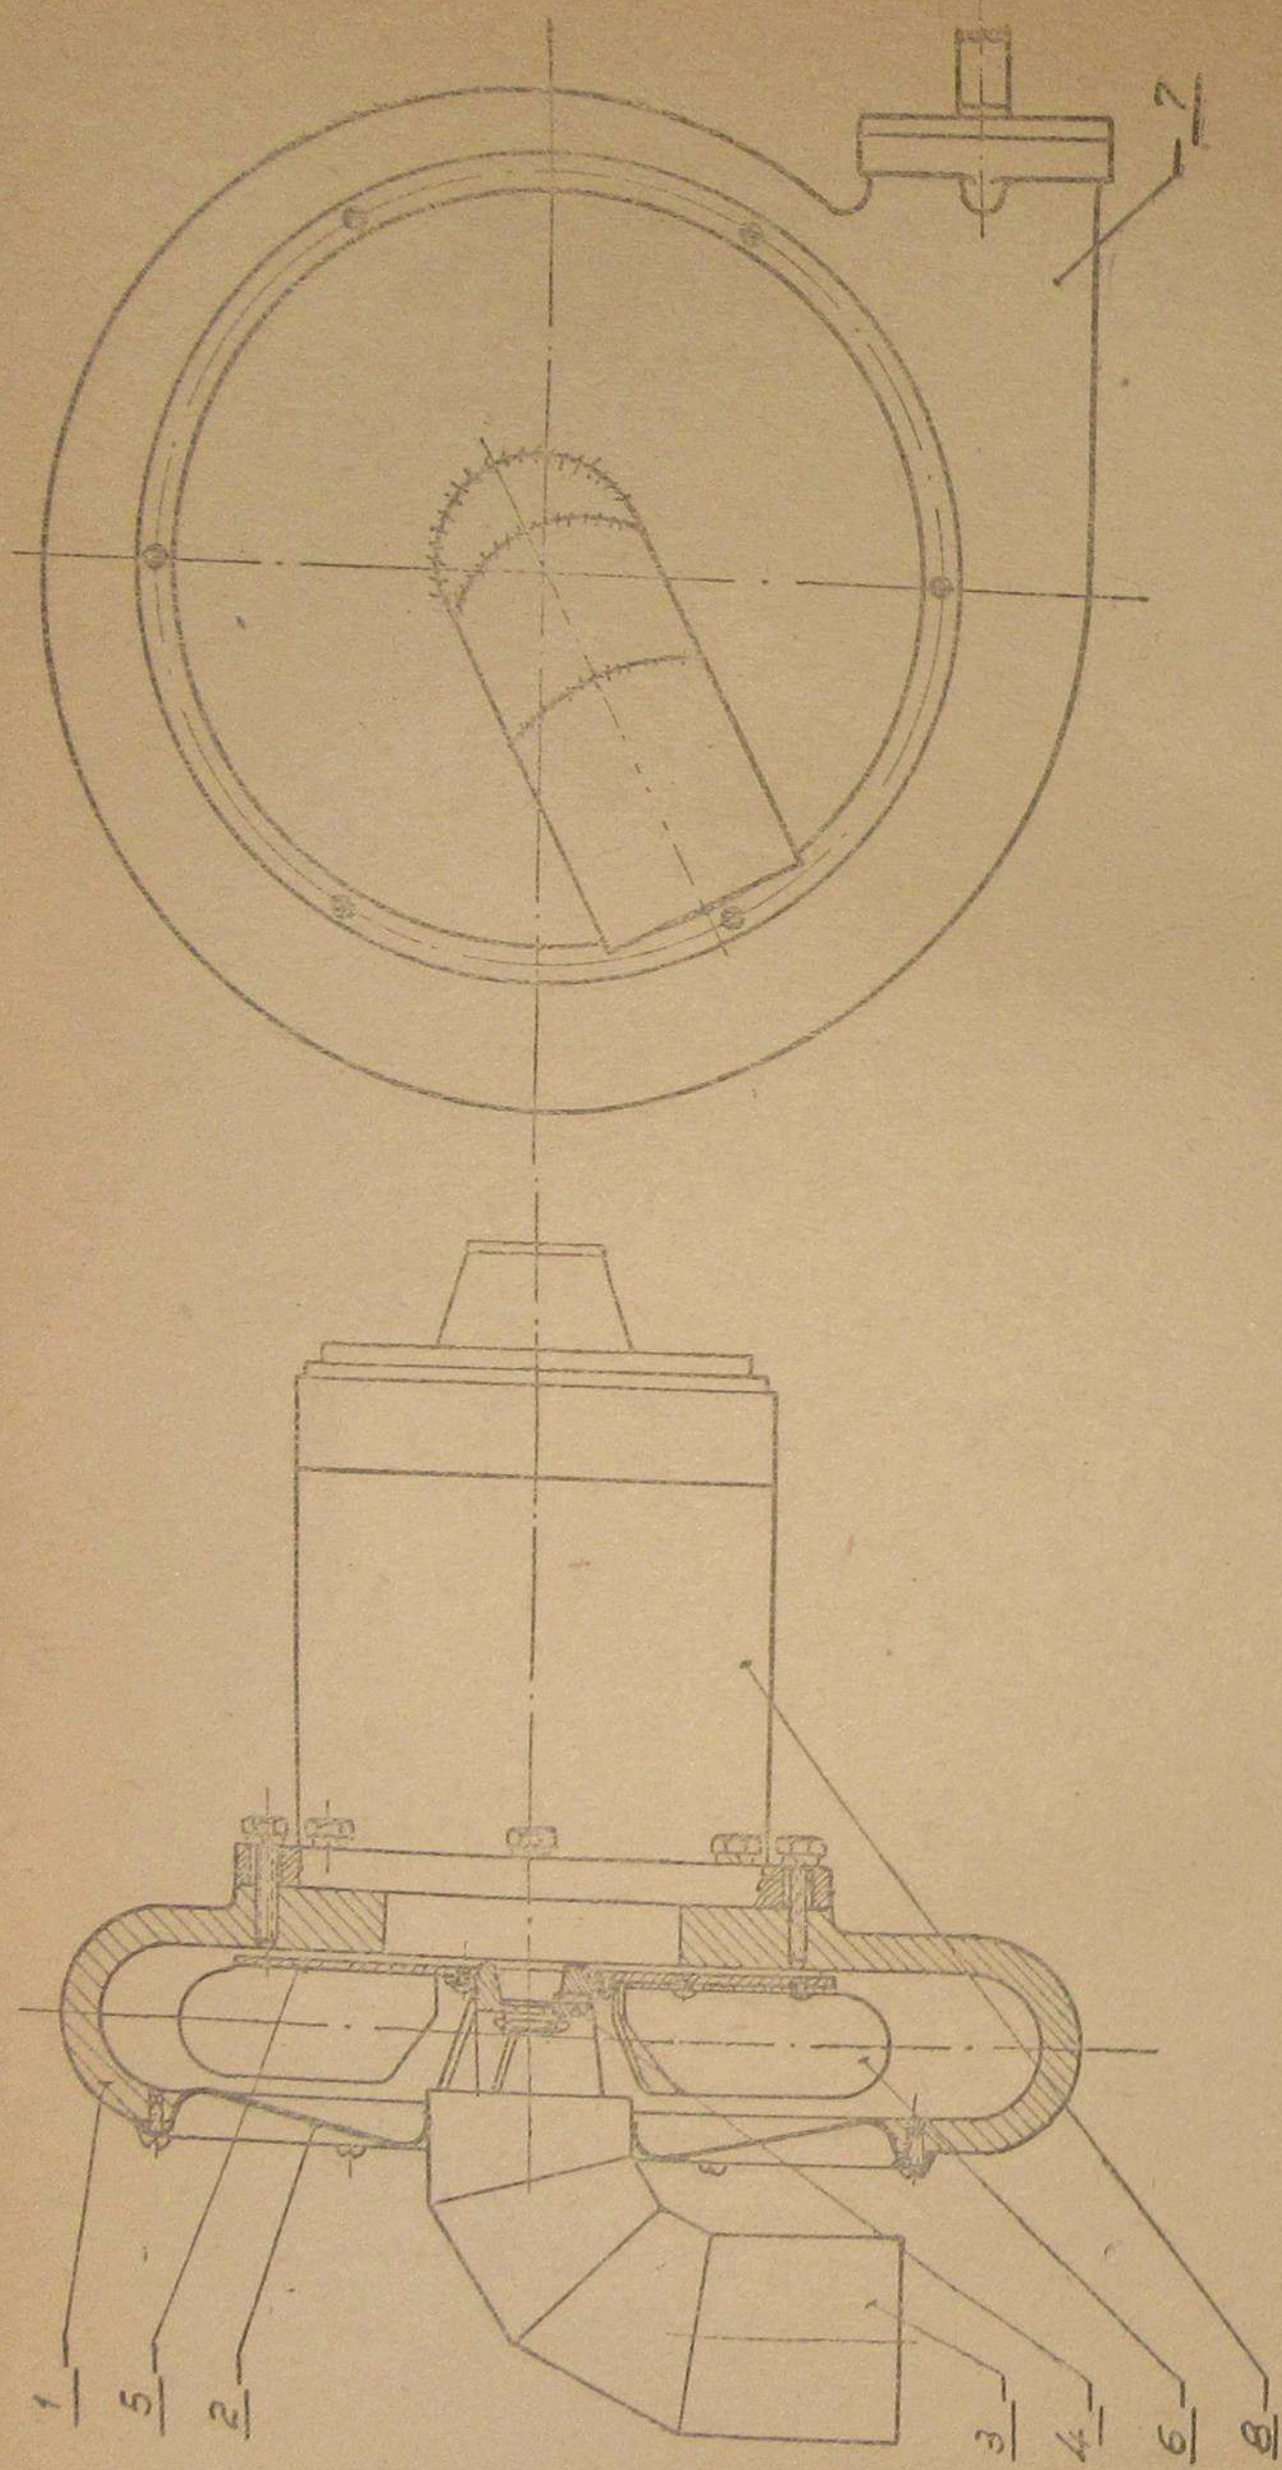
Вентилятор для розжига топлива газогенераторной установки Г69:
